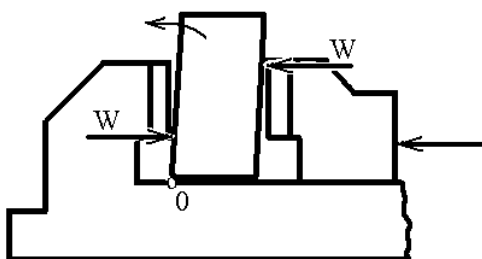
Схема образования погрешности закрепления при установке заготовки в тисках
